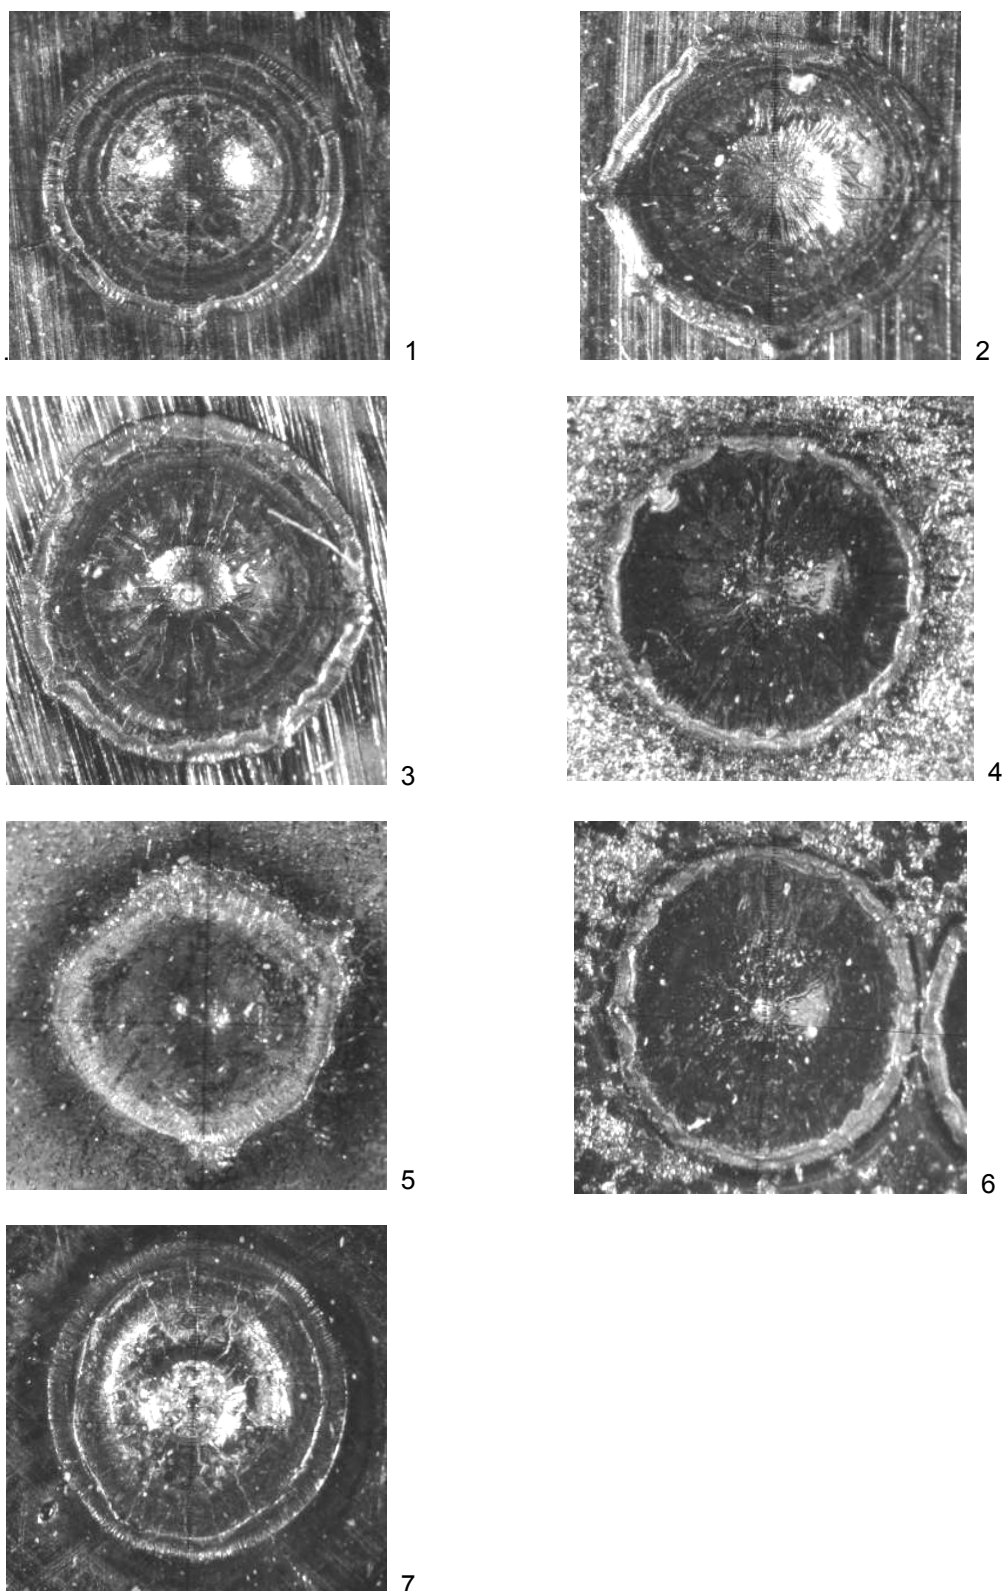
Вид активного пятна (х 25) низковольтного импульсного дугового разряда на поверхности образцов из титановых сплавов ВТ20 (1–3, 5, 7) и ВТ1-00 (4, 6) после различных видов обработки (1 – грубое фрезерование; 2 – чистовое фрезерование; 3 – шабрение; 4 – травление; 5 – элнетроэрозсионная обработка; 6 – травление + УЗ пластическая деформация; 7 – полирование)
